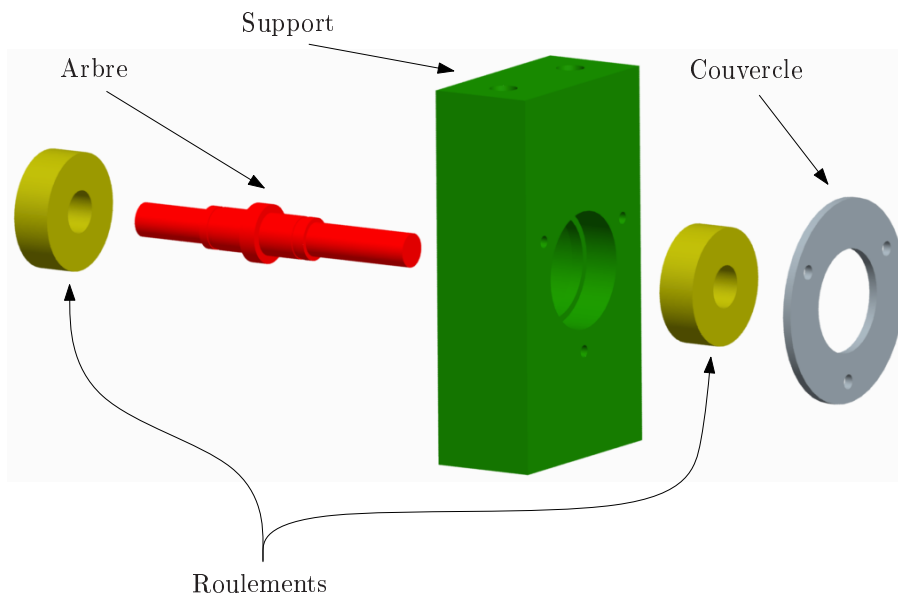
Vue explosée d’un support du capteur d’angle du câble.
